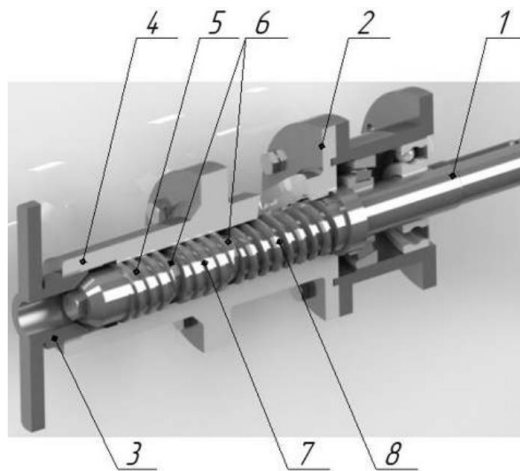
Робоча частина екструдера: 1 – вал екструдера; 2 – корпус зони живлення; 3 – гайка фільтера; 4 – корпус зони екструдуювання. 5 - шнек, що подає; 6 – конічні компресійні кільця; 7 – шнек зони нагрівання; 8 – шнек зони пресування
